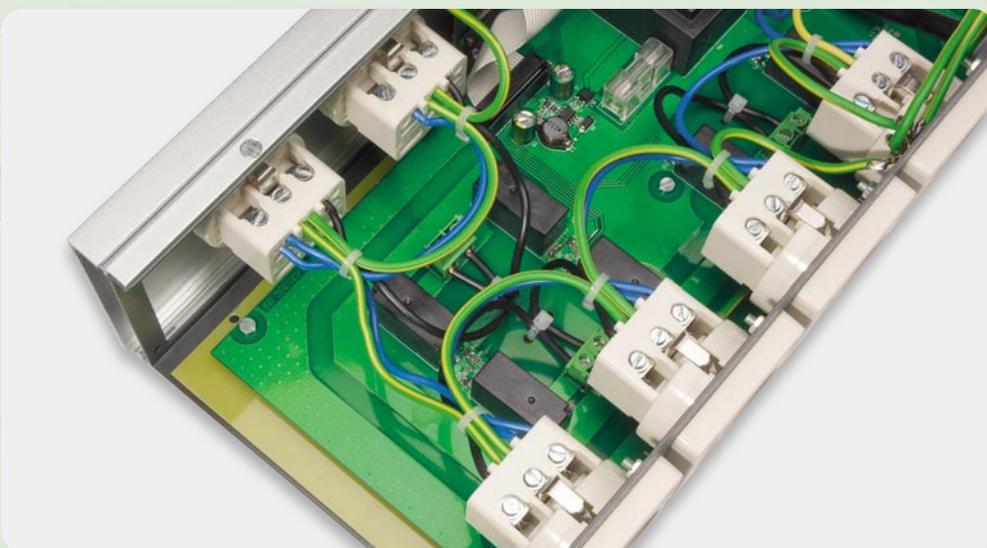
Die Verbindung der vorderen und hinteren Steckdosen. Wichtig auch hier: die Fixierung mit Kabelbindern
